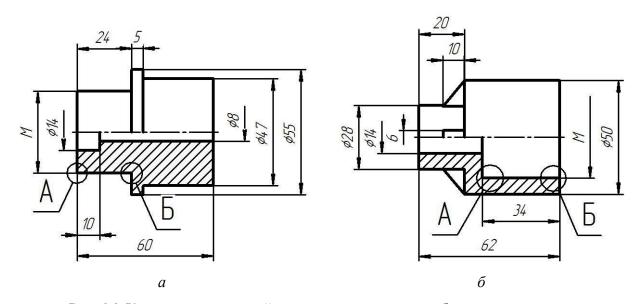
Конструкция деталей, входящих в состав резьбового соединения: a – деталь с наружной резьбой; δ – деталь с внутренней резьбой
